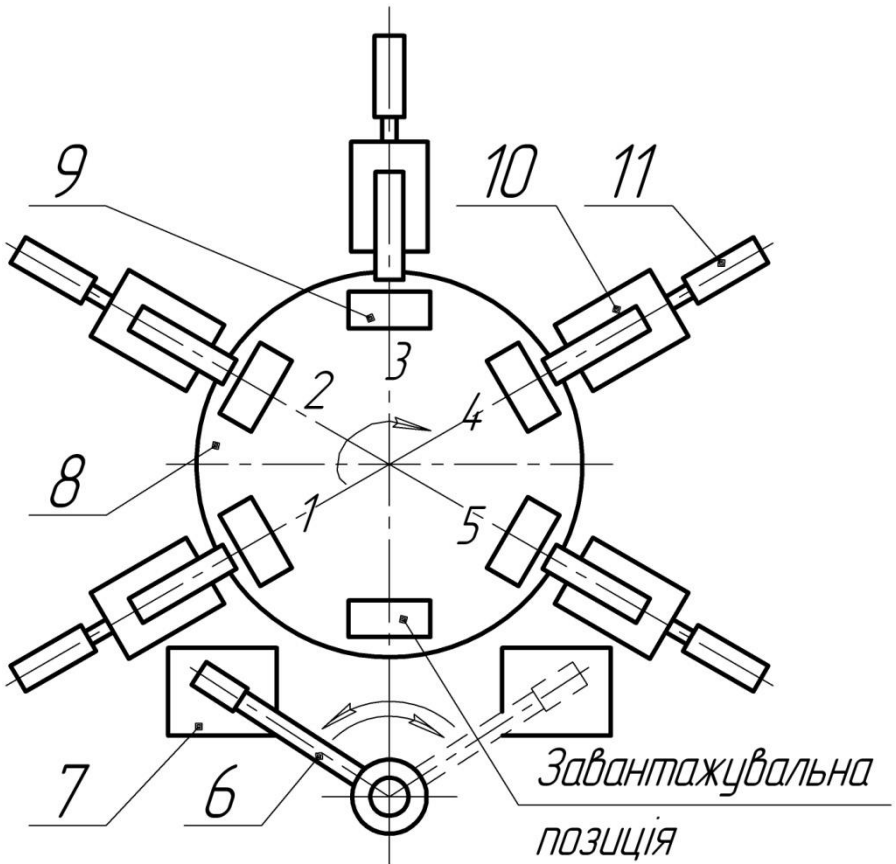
Схема компонування складального багатопозиційного автомата: 1 – 5 – робочі позиції; 6 – маніпулятор; 7 – стіл; 8 – поворотний стіл; 9 – пристрій; 10 – складальна головка; 11 – магазинний пристрій
